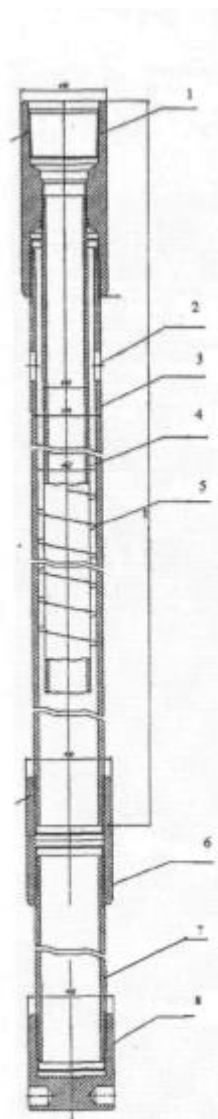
Инерционный десендер УСПШ 1-соединительная муфта, 2- входные отверстия, 3-корпусная труба НКТ, 4 патрубок НКТ48, 5-сепаратор шнековый, 6- муфта НКТ, 7- контейнер для мехпримесей, 8- пробка с резьбой НКТ.
